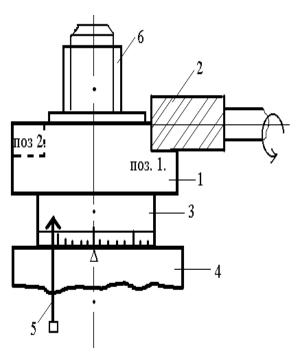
Пример позиции при неизменном установе 1.- заготовка; 2.- фреза; 3.- .поворотное устройство; 4.- основание; 5.- фиксатор; 6.- гайка.
